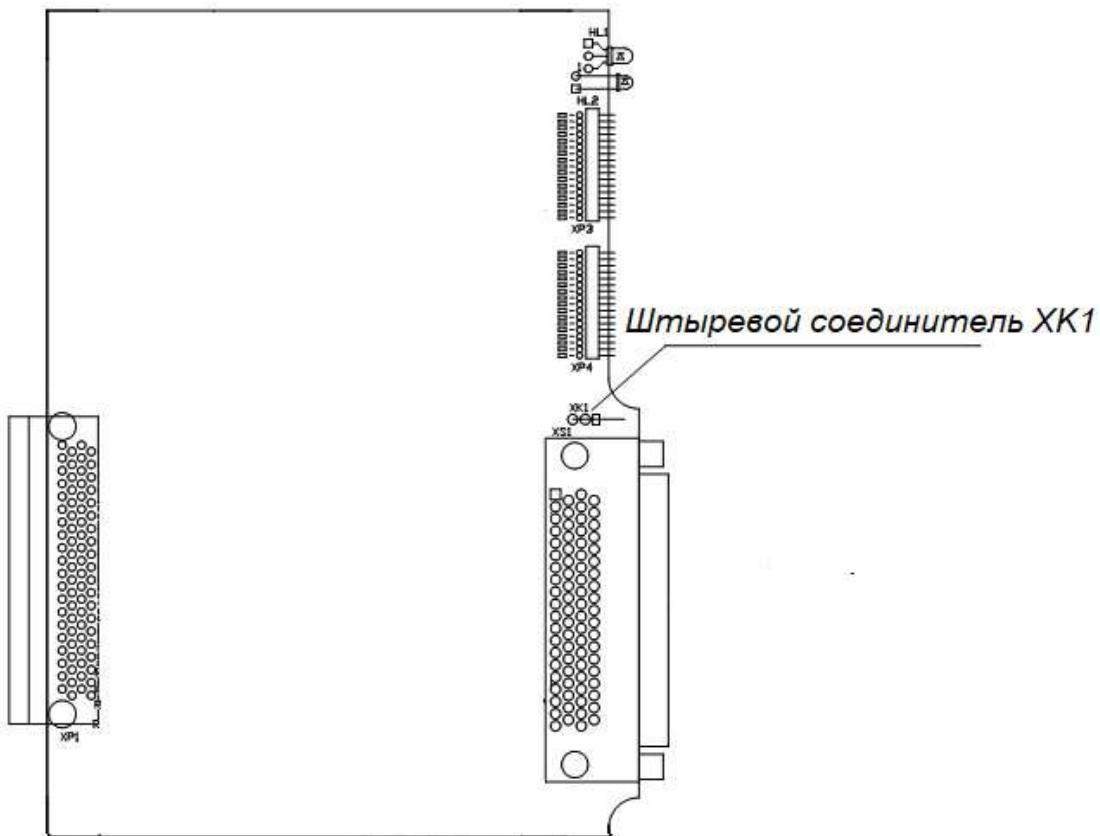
Расположение штыревого соединителя "XK1" на плате модуля TD 715
